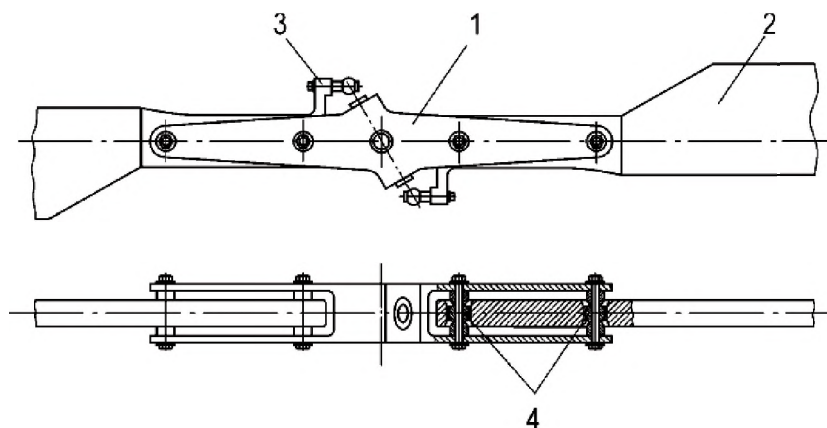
Схема конструкции втулки РВ со сферическими подшипниками в ОШ:
